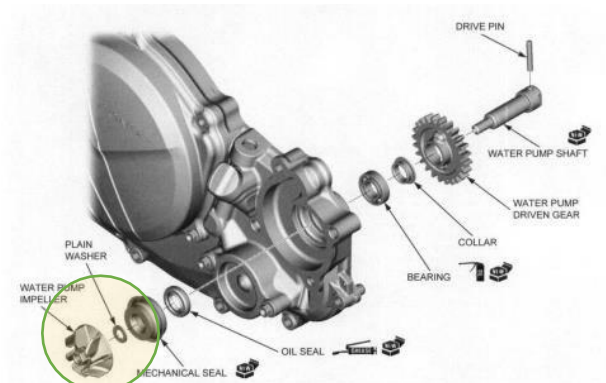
Conjunto de elementos de bomba de agua mecánica [16].
